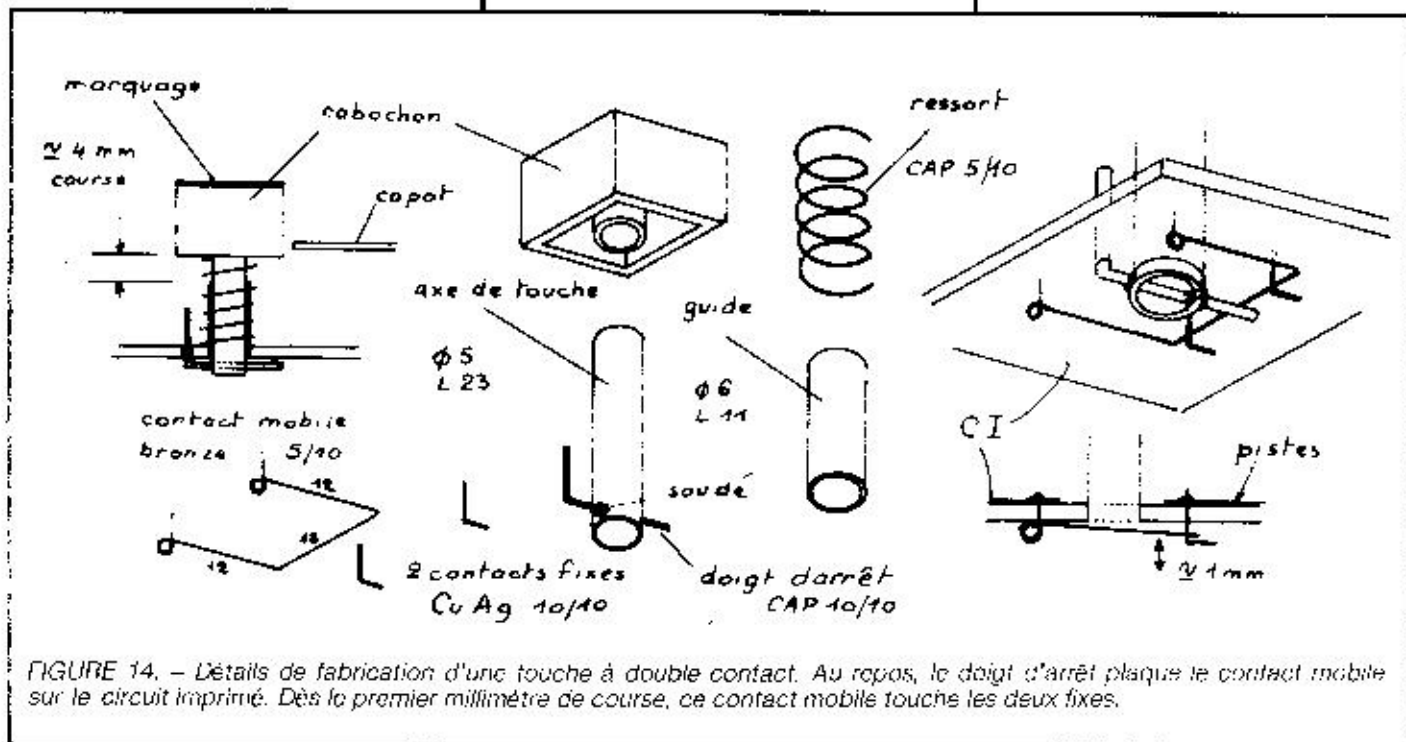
Détails de fabrication d'une touche à double contact. Au repos, le doigt d'arrêt plaquait le contact mobile sur le circuit imprimé. Dès le premier millimètre de course, ce contact mobile touche les deux fixes.
